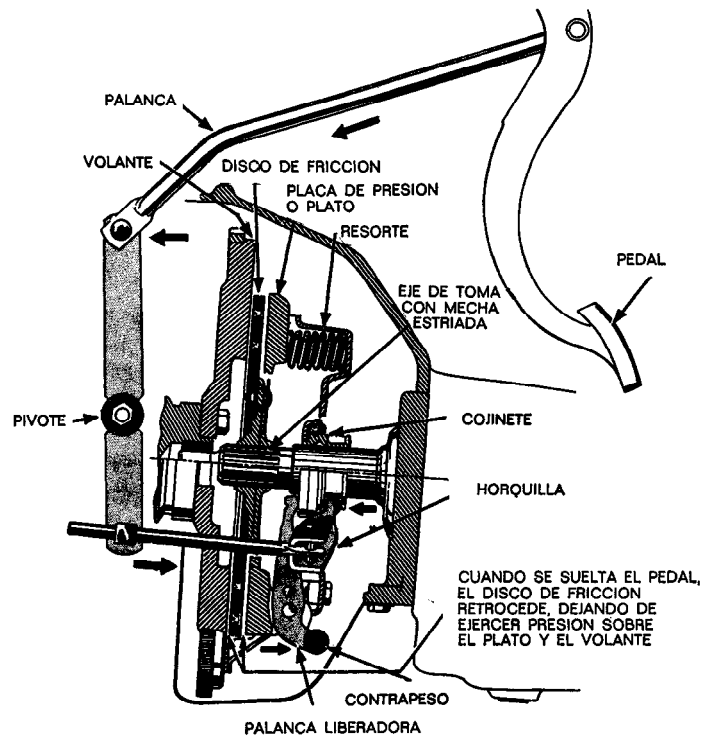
Sección esquemática de un embrague, mostrando el sistema de palancas del pedal (Buick Motor Division of General Motors Corporation).
